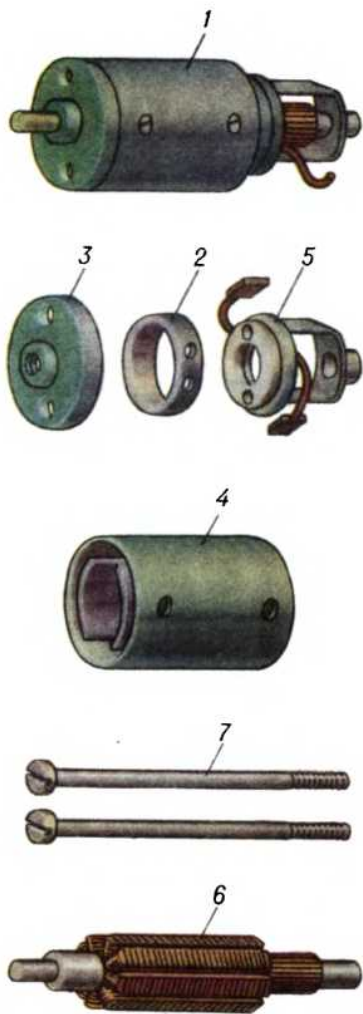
Устройство электродвигателя: 1 — общий вид двигателя; 2 — кожух; 3 — крышка; 4 — корпус с полюсами; 5 — щетки; 6 — якорь с коллектором; 7 — стяжные болты.
